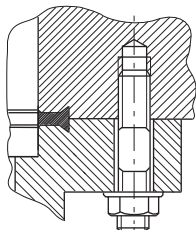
Flanschverbindung CF-F, Stiftschraube und Gewindebohrung
